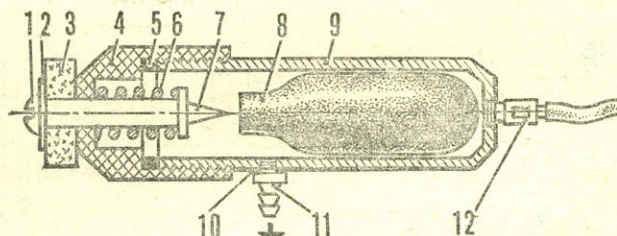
Аккумулятор CO_2 : 1 — винт, 2 — шайба, 3 — сахар, 4 — крышка (фторопласт), 5 — прокладка (резина), 6 — пружина, 7 — игла, 8 — сифонный баллон, 9 — корпус, 10 — резиновое кольцо, 11 — штуцер, 12 — предохранительный клапан (велонишпель).
